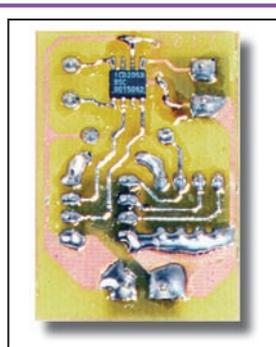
Vue de la même platine mais du côté soudures. Voyez comment est monté le circuit intégré ICD2053B.
